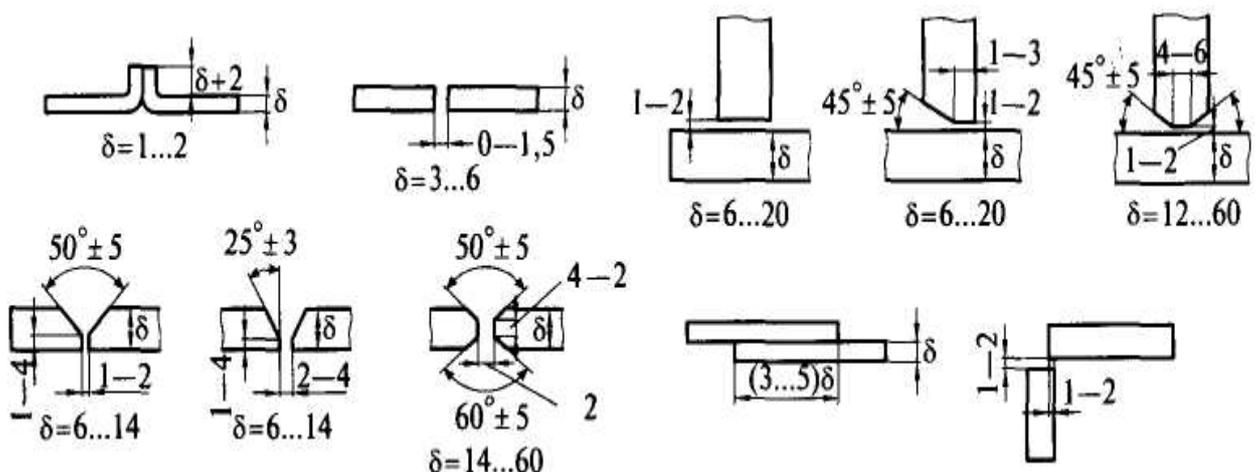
Разделка кромок под сварку элементов различной толщины
